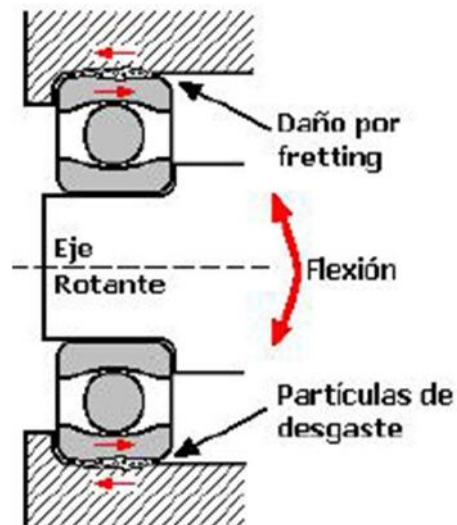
Origen de desgaste por fretting en un rodamiento. [i]
